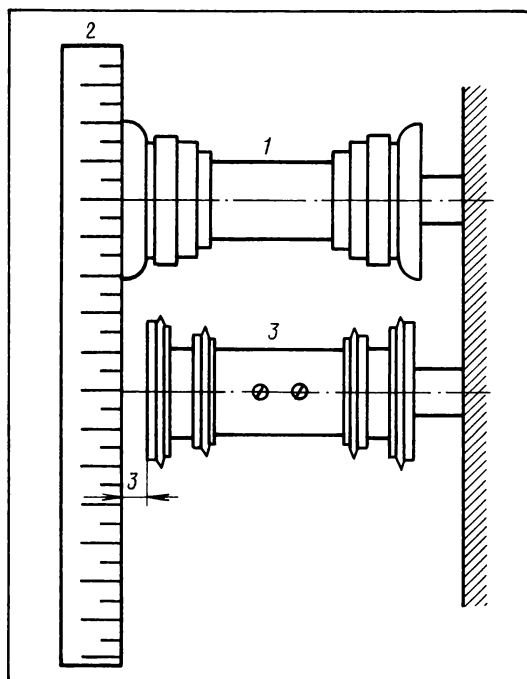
Проверка положения гладкого барабана: 1 — гладкий барабан магнитного звукового блока; 2 — металлическая линейка; 3 — верхний тянущий двухформатный барабан
